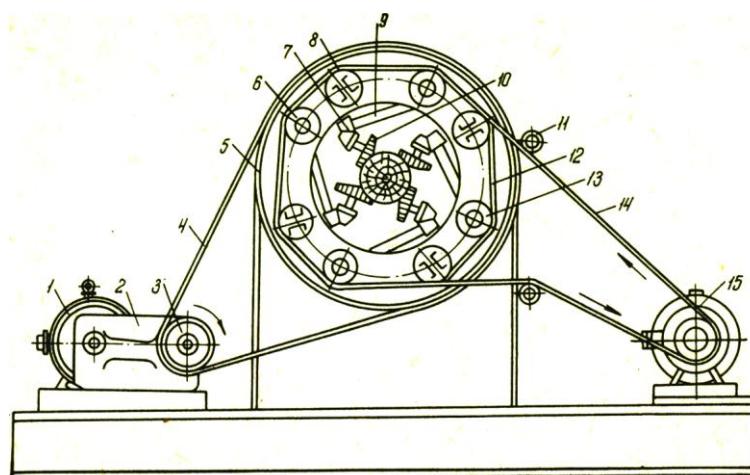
Схема привода головки чистой окорки станка 2OK63-2:
